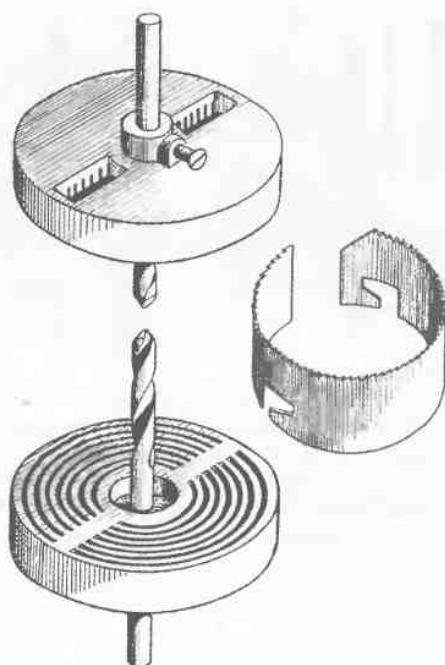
, а. Вторая конструкция кругореза заводского изготовления: вид сверху и вид снизу; полотно сменной пилки (вид снизу)
